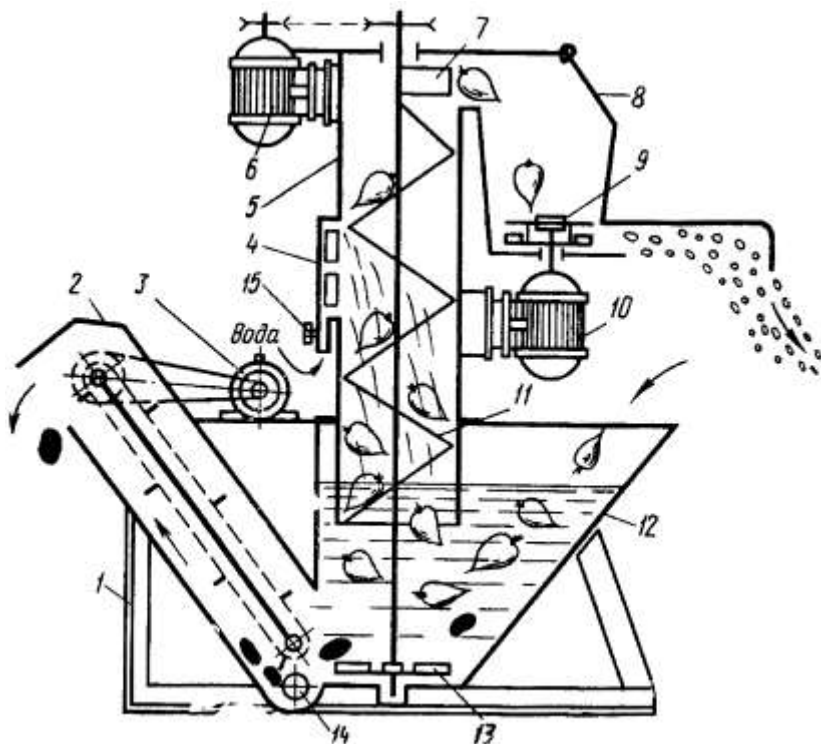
Схема подрібнювача-каменеуловлювача ИКМ-5: 1 – рама; 2 – транспортер скребковий; 3 – мотор-редуктор; 4 – колектор підведення води; 5 – кожух шнекової мийки; 6, 10 – електродвигуни; 7 – викидач; 8 – кришка подрібнювача; 9 – подрібнювач; 11 – шнек; 12 – ванна; 13 – крилач; 14 – люк; 15 – вентиль.
